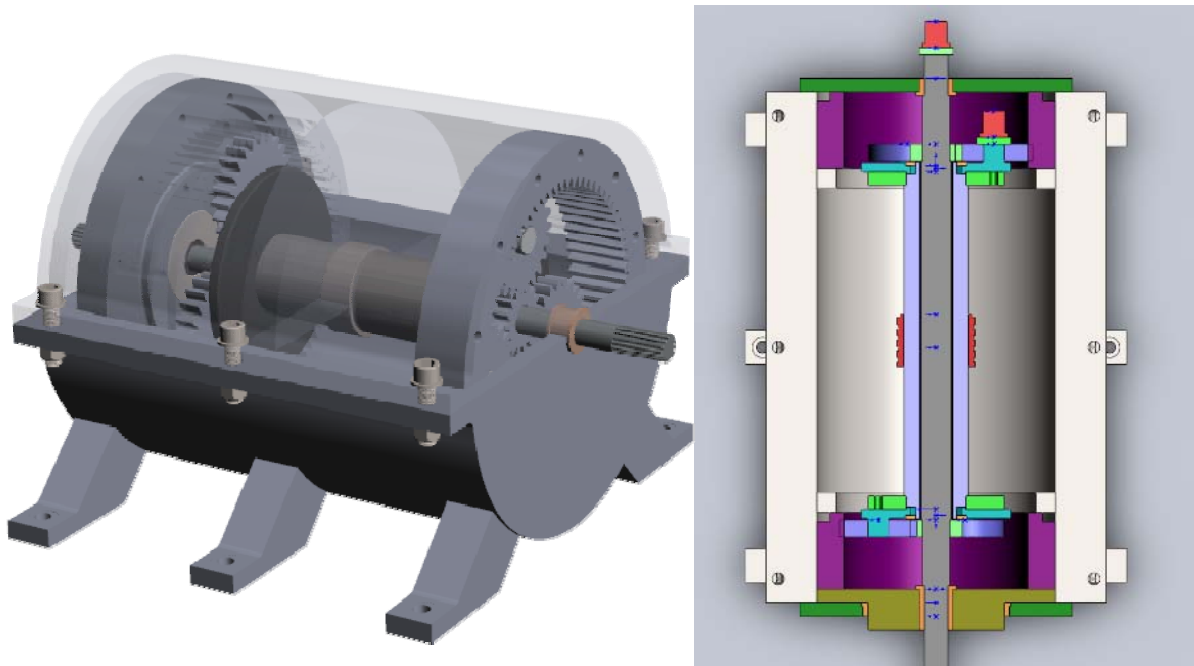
Vista del banco de ensayo a construir y corte en planta del mismo
